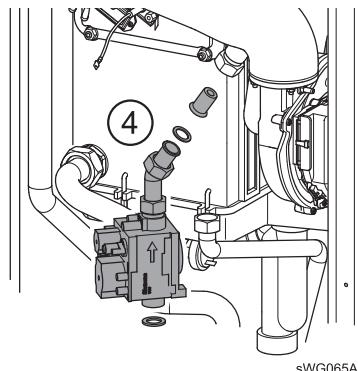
Défaire les conduites de branchement (WGB 50 E)
